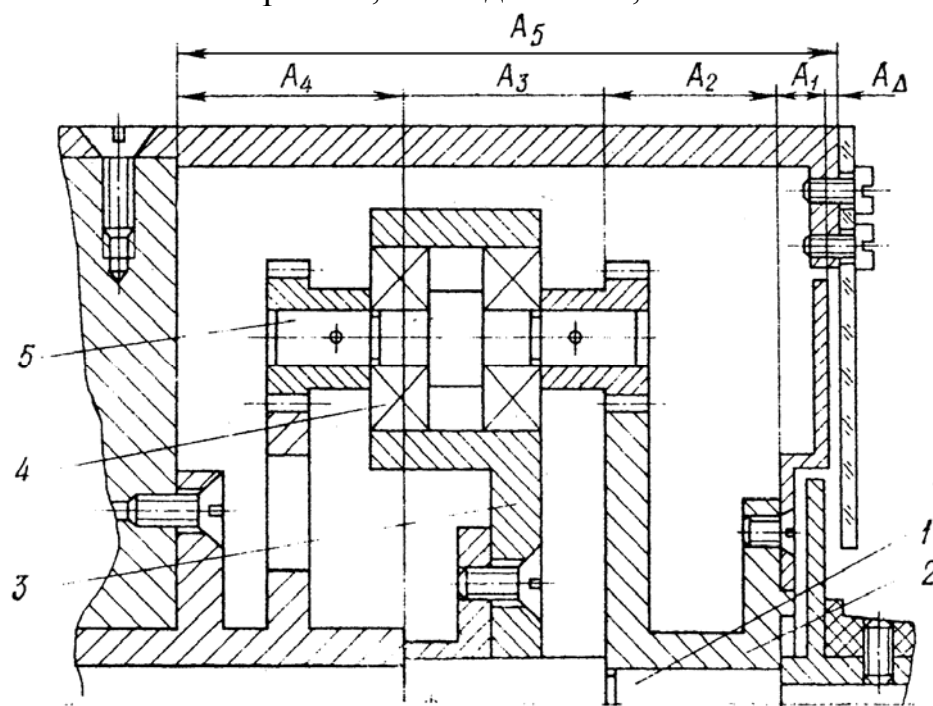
Узел подшипникового соединения: 1 – вал; 2 – колесо; 3- водило; 4 – подшипник; 5 – ось
